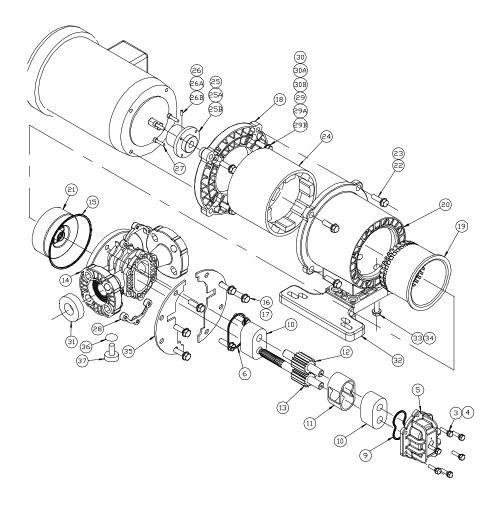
IMAGEM EXPLODIDA DA BOMBA E75 E E125
